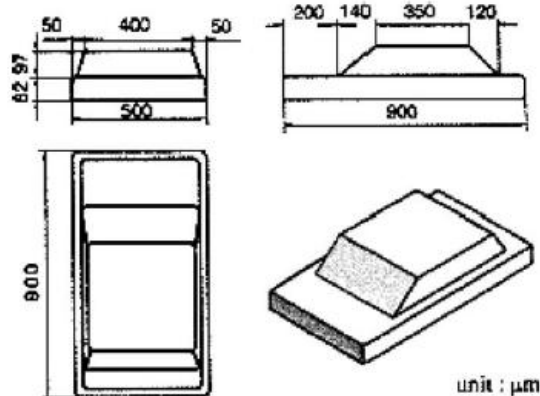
Pieza final del micro-estampado con martillo incremental, ver referencia [3].
